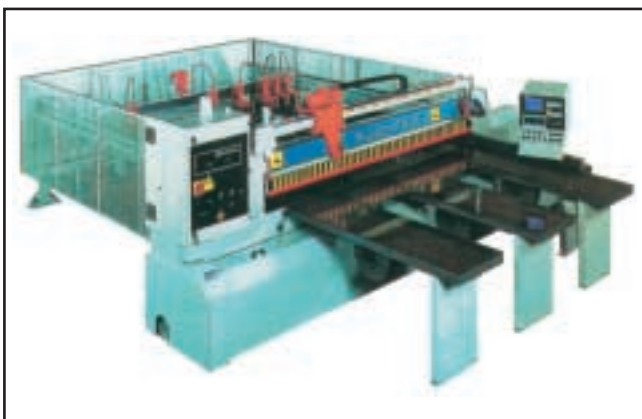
a) - La macchina Euromac per squadrare e fresare
